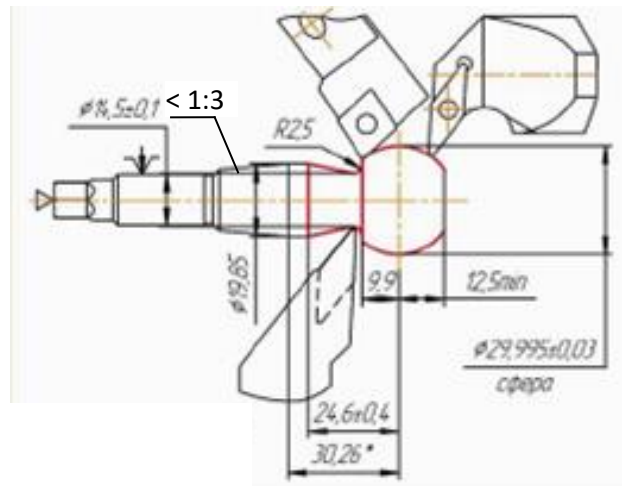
Типова оброблювана деталь, яка має різні поверхні обертання-палець кульовий
